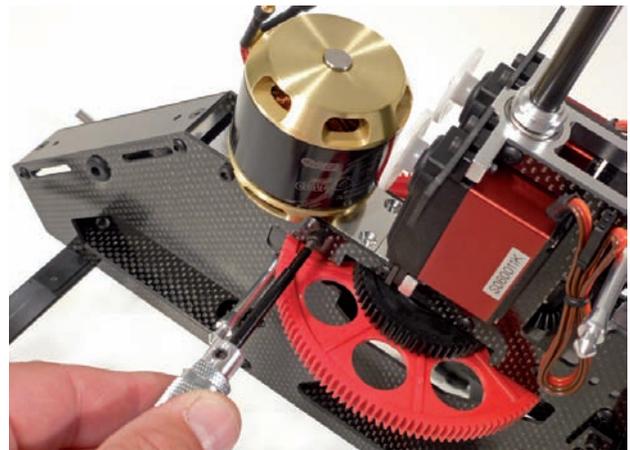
Nachdem die Montageplatte in Position gebracht wurde, ist sie mit insgesamt sechs Schrauben mit dem Rahmen zu verschrauben.
